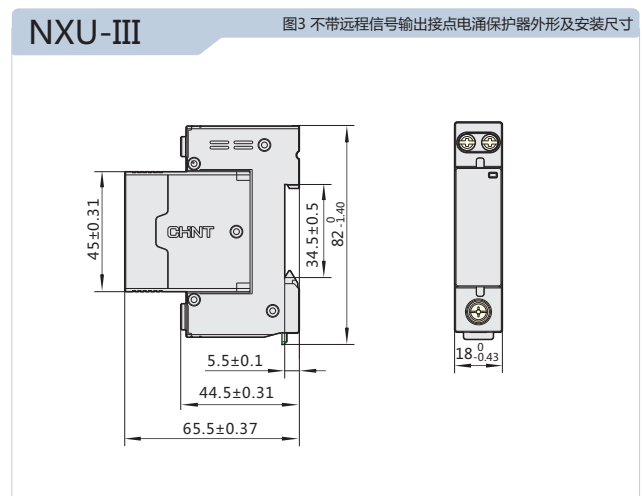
不带远程信号输出接点电涌保护器外形及安装尺寸
